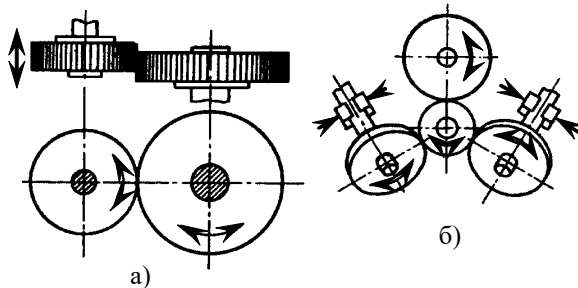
Схема притирання зубів циліндричних зубчастих коліс:
